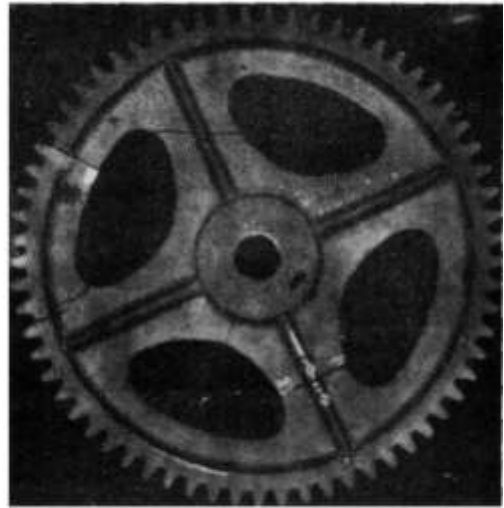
Частина сталевого виливка, яка має декілька дефектів: залив – проникнення металу зазорами стрижневих знаків; поверхнєве ушкодження – недбале транспортування виливка; газова шорсткість – сира форма (табл.3.1, поз.2.5; 2.9; 2.12)
